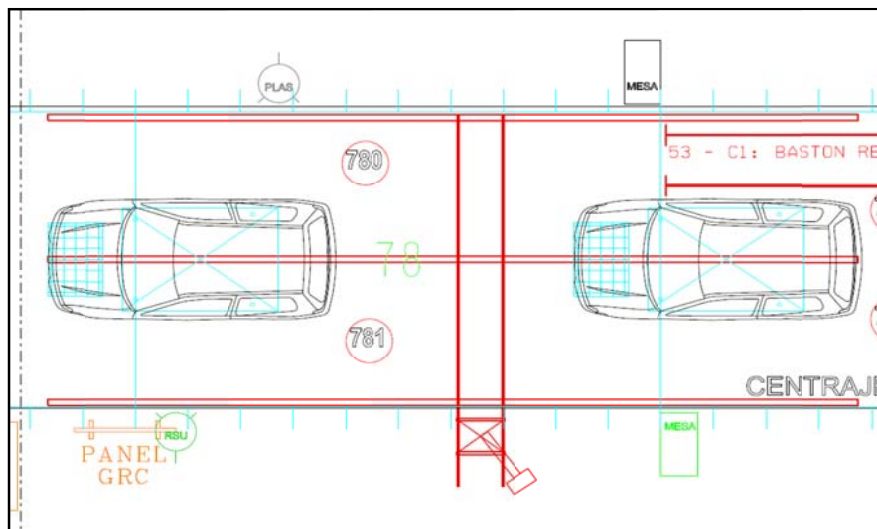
Layout manipulador montaje de butacas (opción 2)
